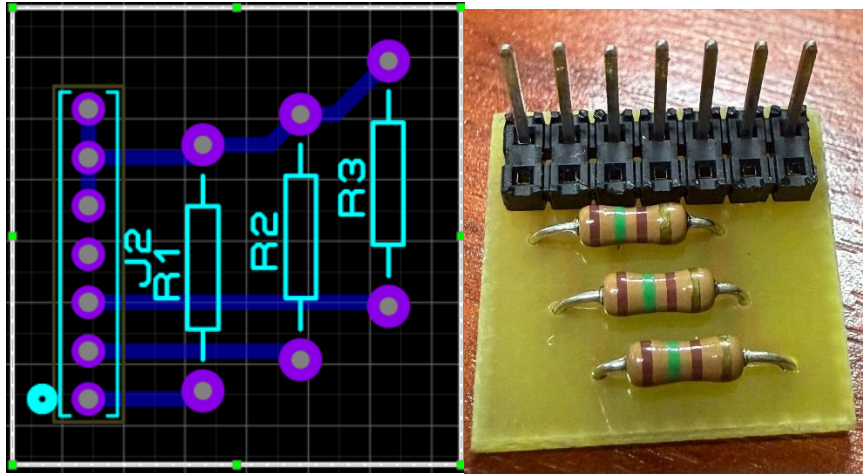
Placa PCB que sustituye módulo terminal del ET200S
